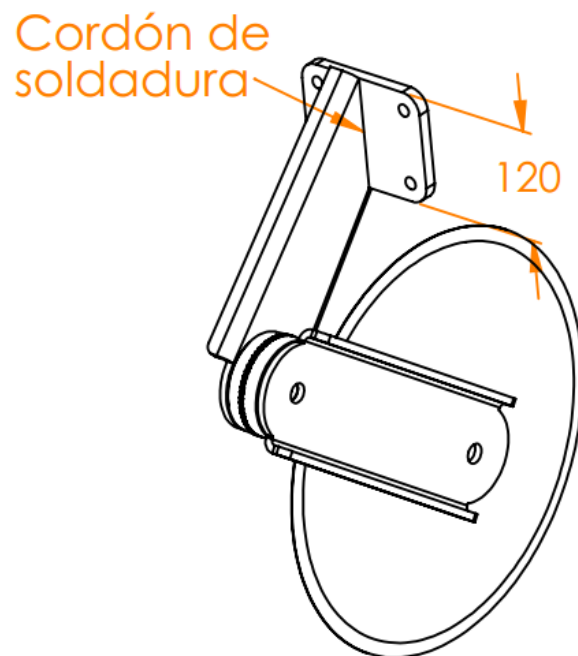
cordón de soldadura unión brazo superior con placa perforada. Elaboración propia.
